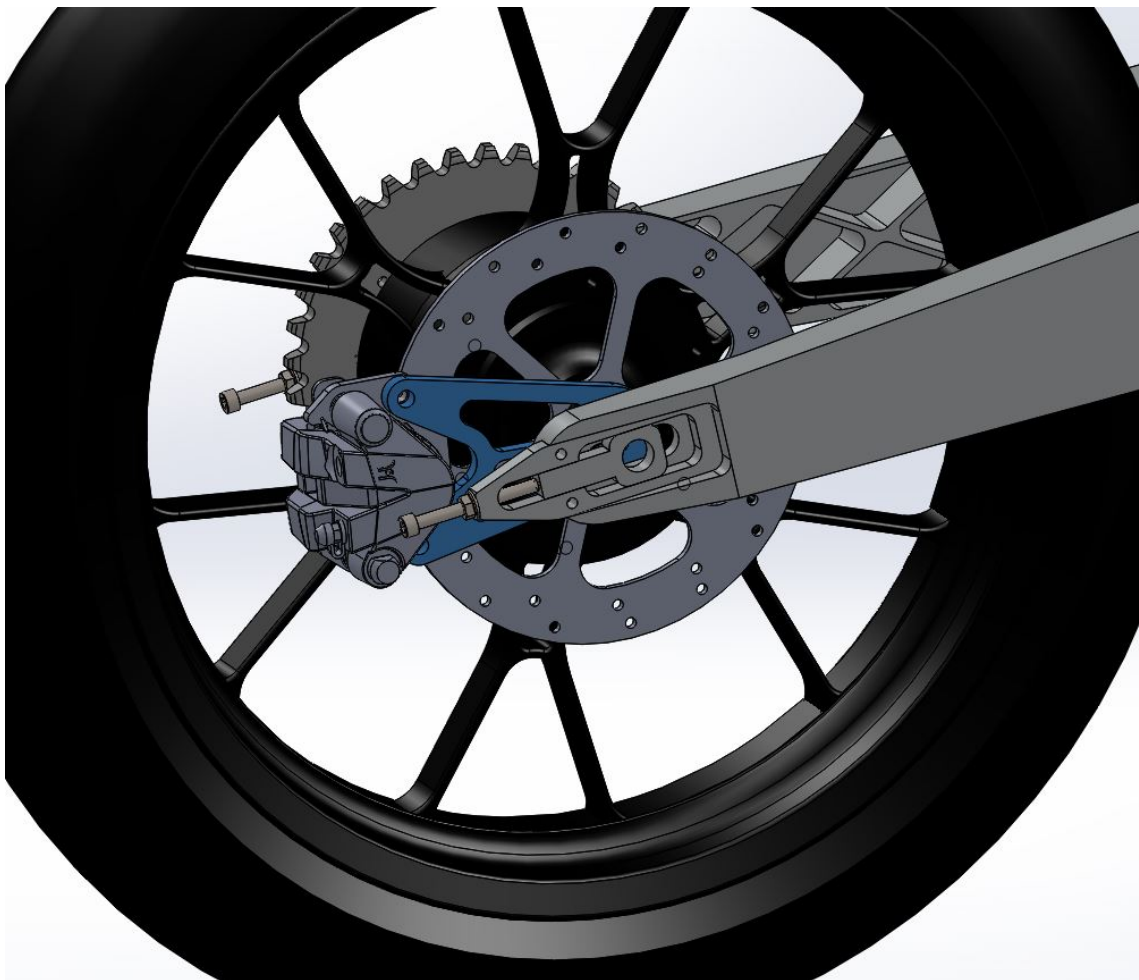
Fabricación. Ensamblaje. Vista cercana.
